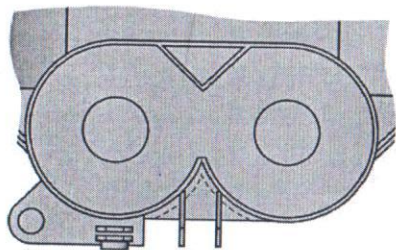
Контроль околошовных зон сварного соединения боковых стенок и поддона центральной люлочной подвески
